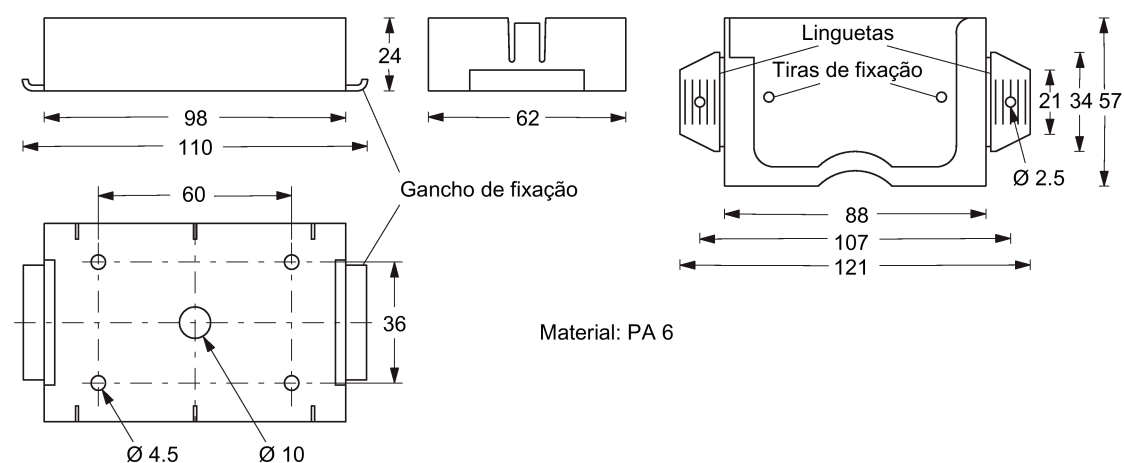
Desenho de dimensões do espaçador 6GT2190-0AA00 com bolsa de fixação 6GT2190-0AB00
